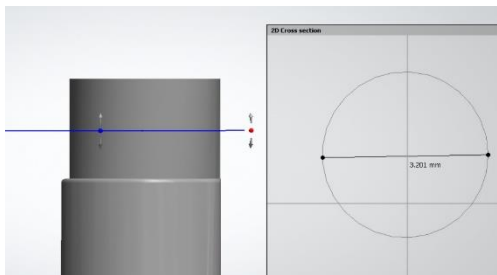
Dimensión superior de la camisa diseñada en CAD
